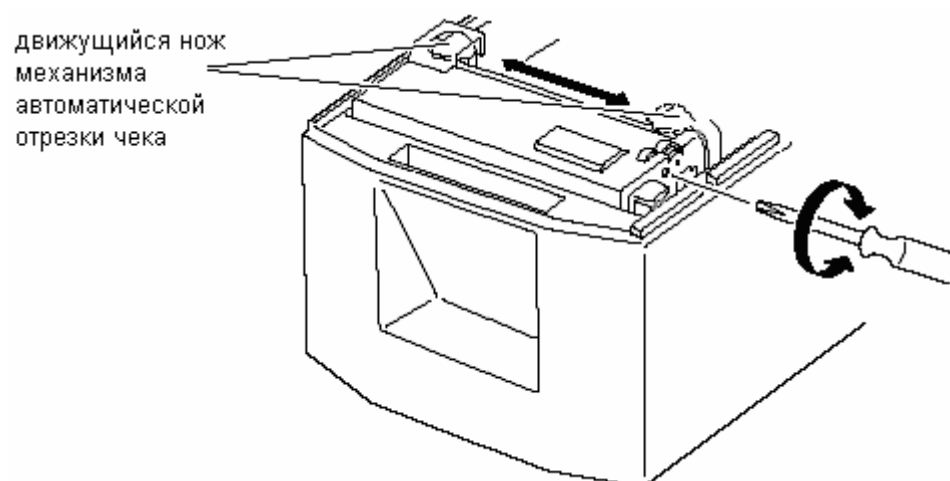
Винт регулировки ножа автоматической отрезки чека
